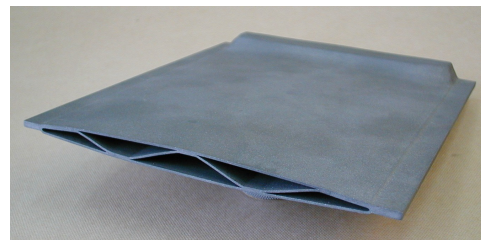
Модель полый лопатки, изготовленная совмещением сверхпластической формовки и сварки давлением при 750°C, из наноструктурного сплава ВТ6 в условиях низкотемпературной СП.
